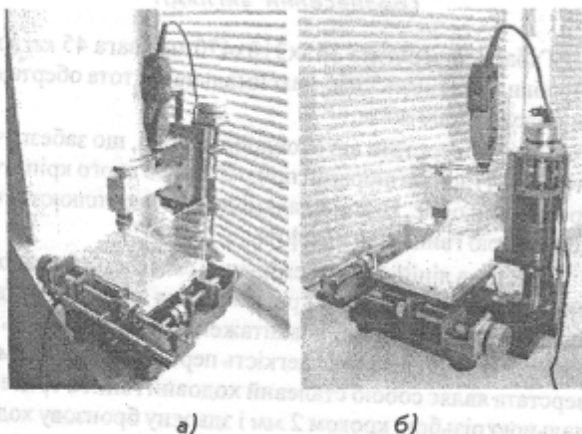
Загальний вигляд верстата: а — спереду; б — збоку.
